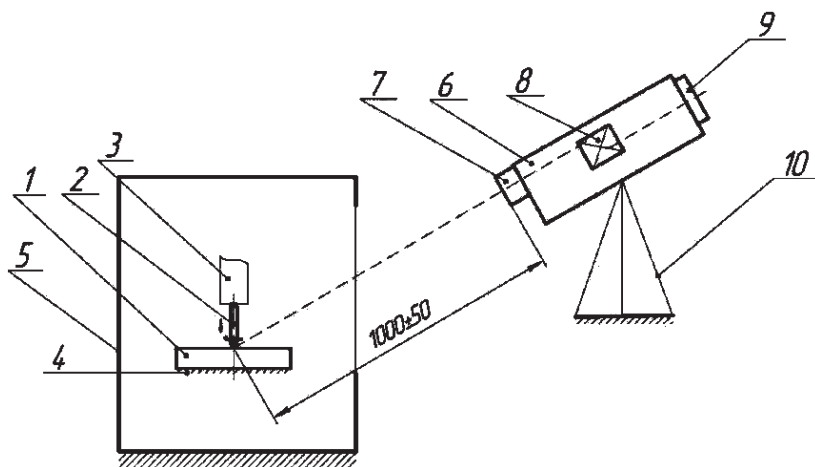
Схема взаимного расположения обрабатывающего центра — образца — тепловизора: 1 — образец; 2 — рабочий режущий инструмент; 3 — зажимной патрон; 4 — рабочий стол центра; 5 — обрабатывающий центр с ЧПУ; 6 — тепловизор; 7 — объектив; 8 — оптико-цифровой преобразователь; 9 — видоискатель; 10 — опора
